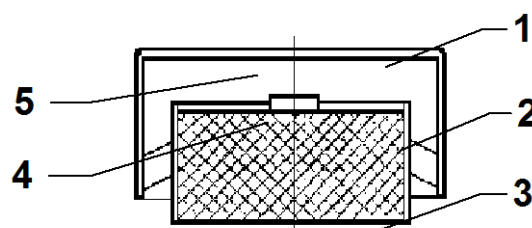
Конструкція генератора ОСА-М з коаксіально розташованими напівкорпусами:
